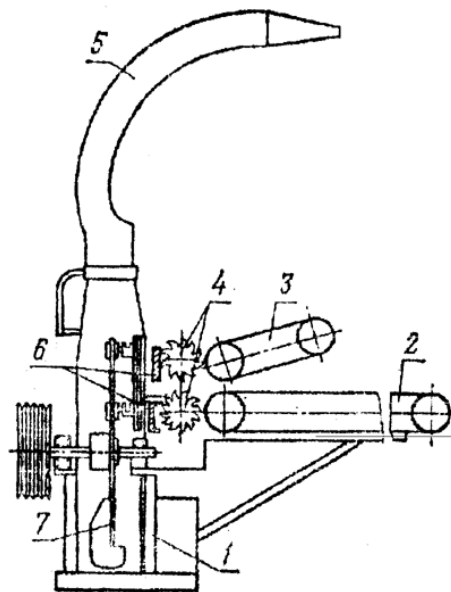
Схема соломорізки РСС-6Б: 1-рама; 2-транспортер; 3-підпресовуючий транспортер; 4-вальці; 5-дефлектор; 6-протиризальна пластина; 7-диск з ножами і лопатками
